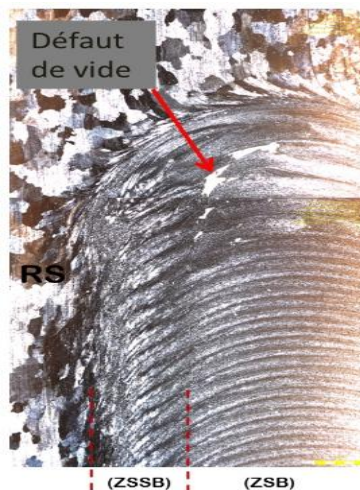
Observation de Défaut de vide sur le cordon de soudage [52].
